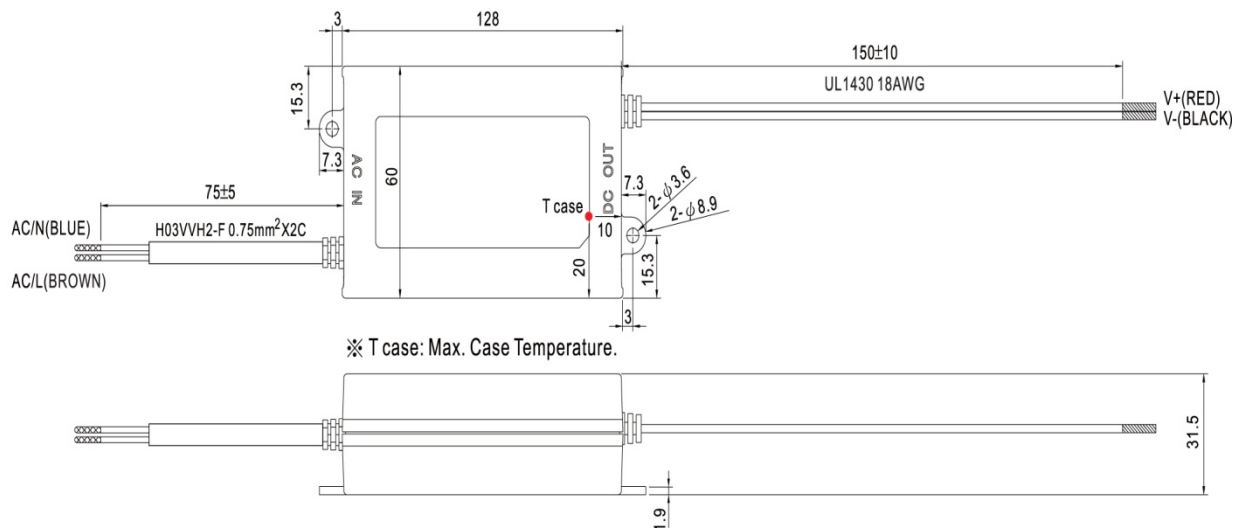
Габаритные и присоединительные размеры драйвера PLD-40-350B
